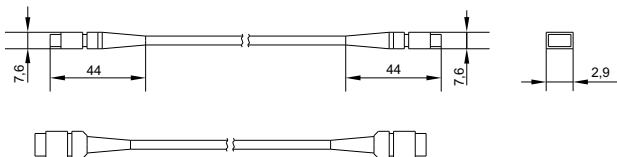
Внешний вид сборки кабельной / Figure 1 – Appearance of the trunk cable /
